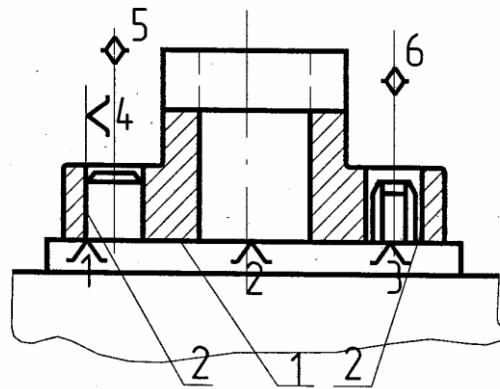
Базирование корпусной заготовки на плоскость и два отверстия
